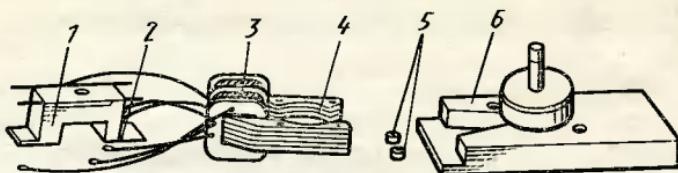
Статор электродвигателя с приспособлением для сборки:
